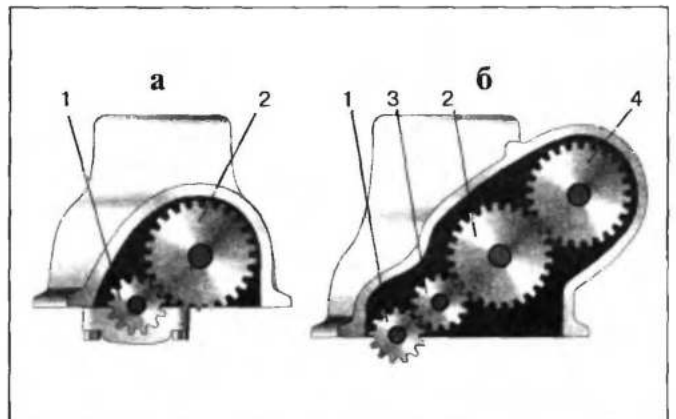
Шестеренный привод распределительного вала: а — бензиновый двигатель OHV; б — дизель; 1 — ведущая шестерня коленчатого вала; 2 — ведомая шестерня (распределительного вала); 3 — паразитная шестерня; 4 — шестерня привода топливного насоса высокого давления
